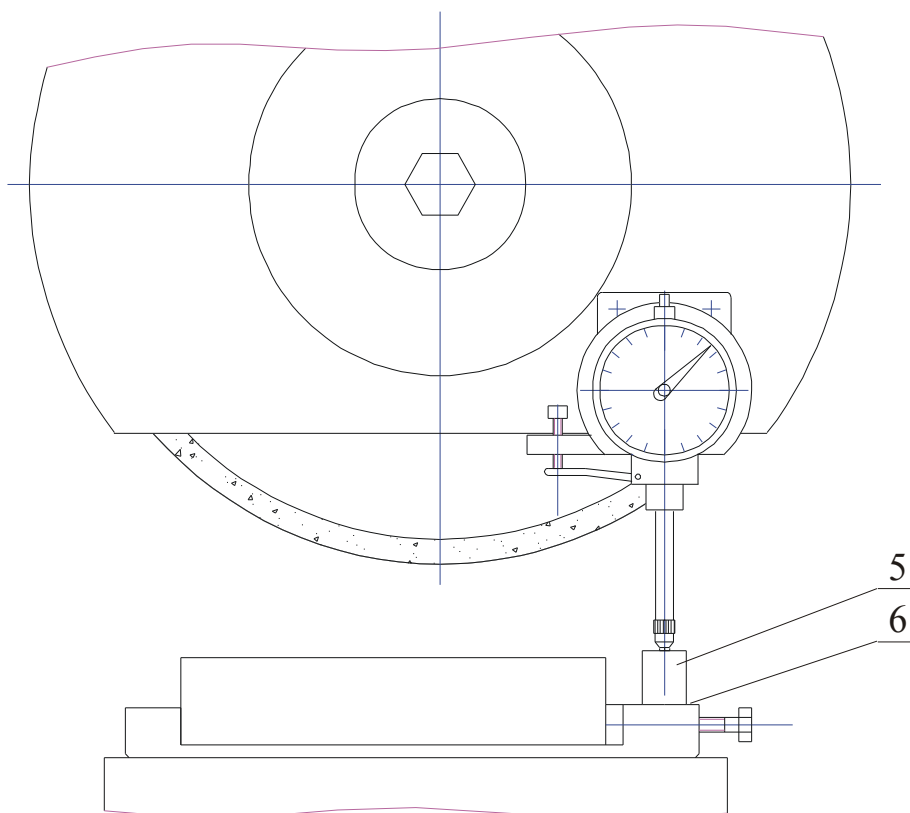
Схема установки базы индикатора перед измерением высоты образца
